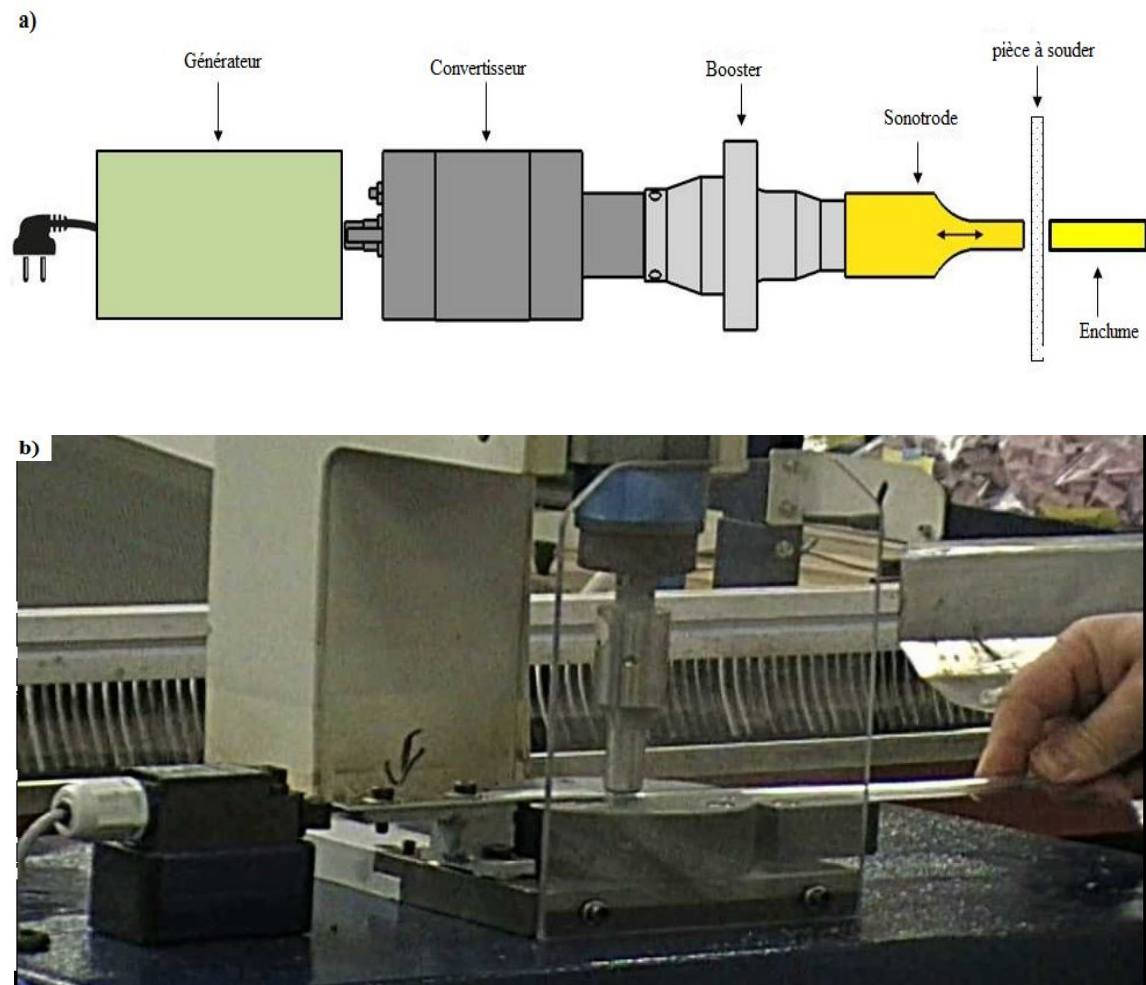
Soudage par ultrasons : a) schéma du procédé b) machine de soudage
